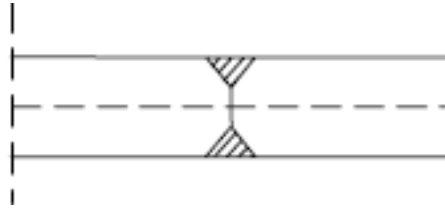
47 Tipo de soldaduras en el bastidor
